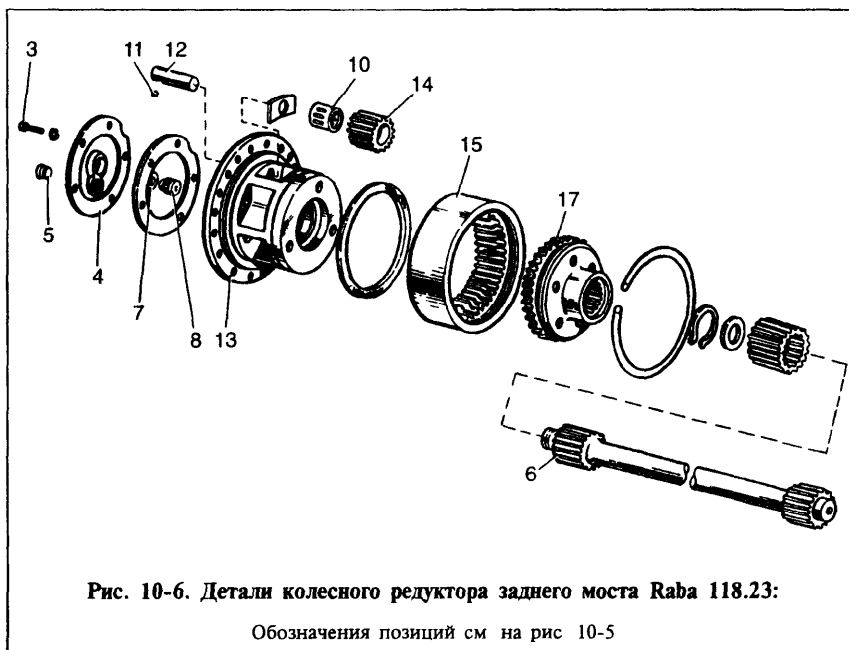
Детали колесного редуктора заднего моста Raba 118.23:
